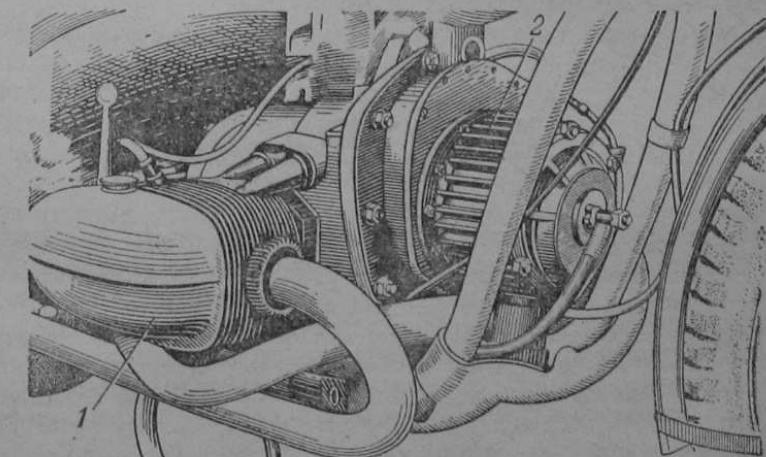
Установка нагнетателя впереди двигателя М-35К:
